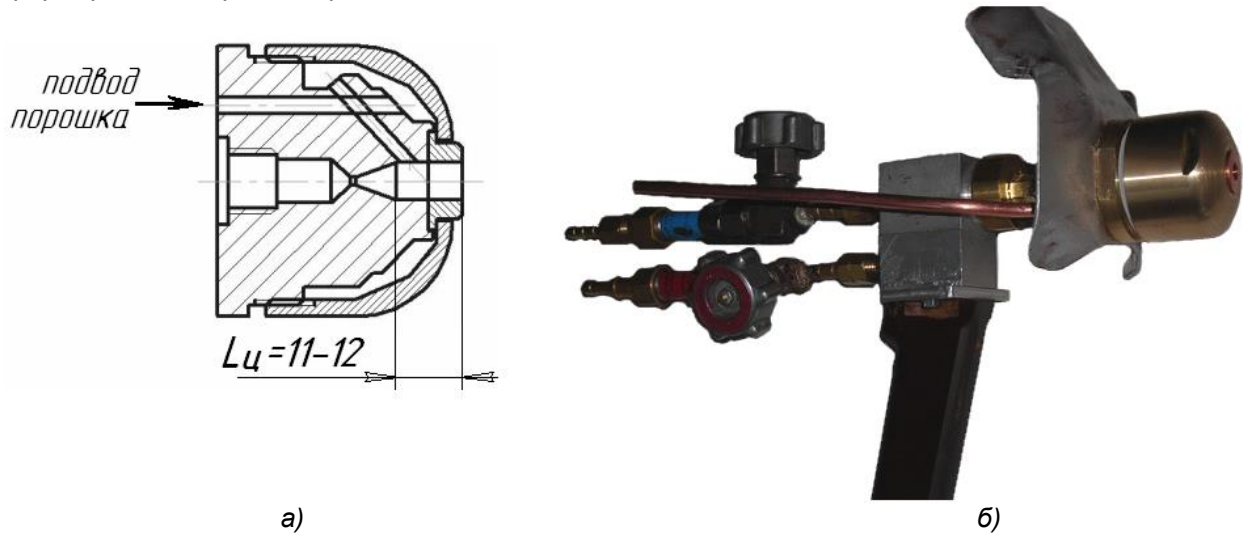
Универсальное устройство для СГП-наплавки: а - схема сопла для СГП-наплавки; б – наплавочное устройство с универсальным соплом в сборе
